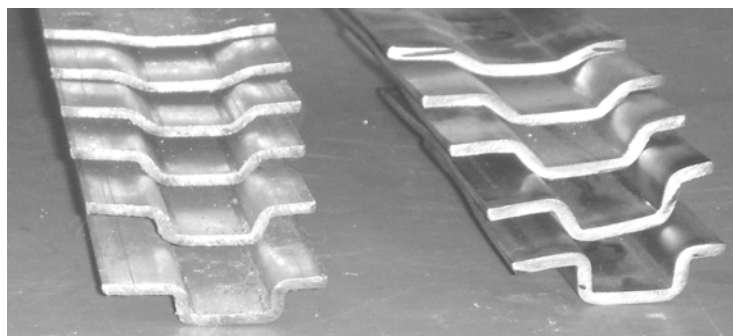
Образцы профилей по переходам (слева направо) с постоянными радиусами формовки и с переменными промежуточными радиусами формовки
